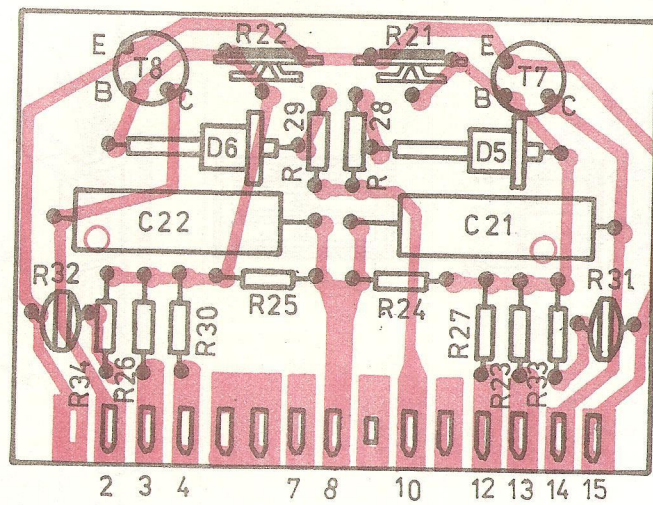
Deska zdrojová 3AK 061 41 (strana spojů)
